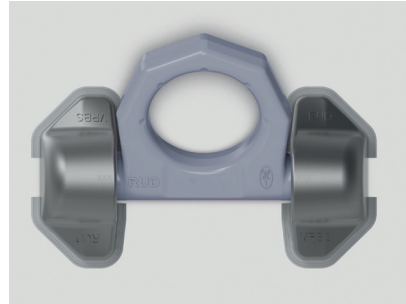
Anschweißklotz 2 anschweißen
